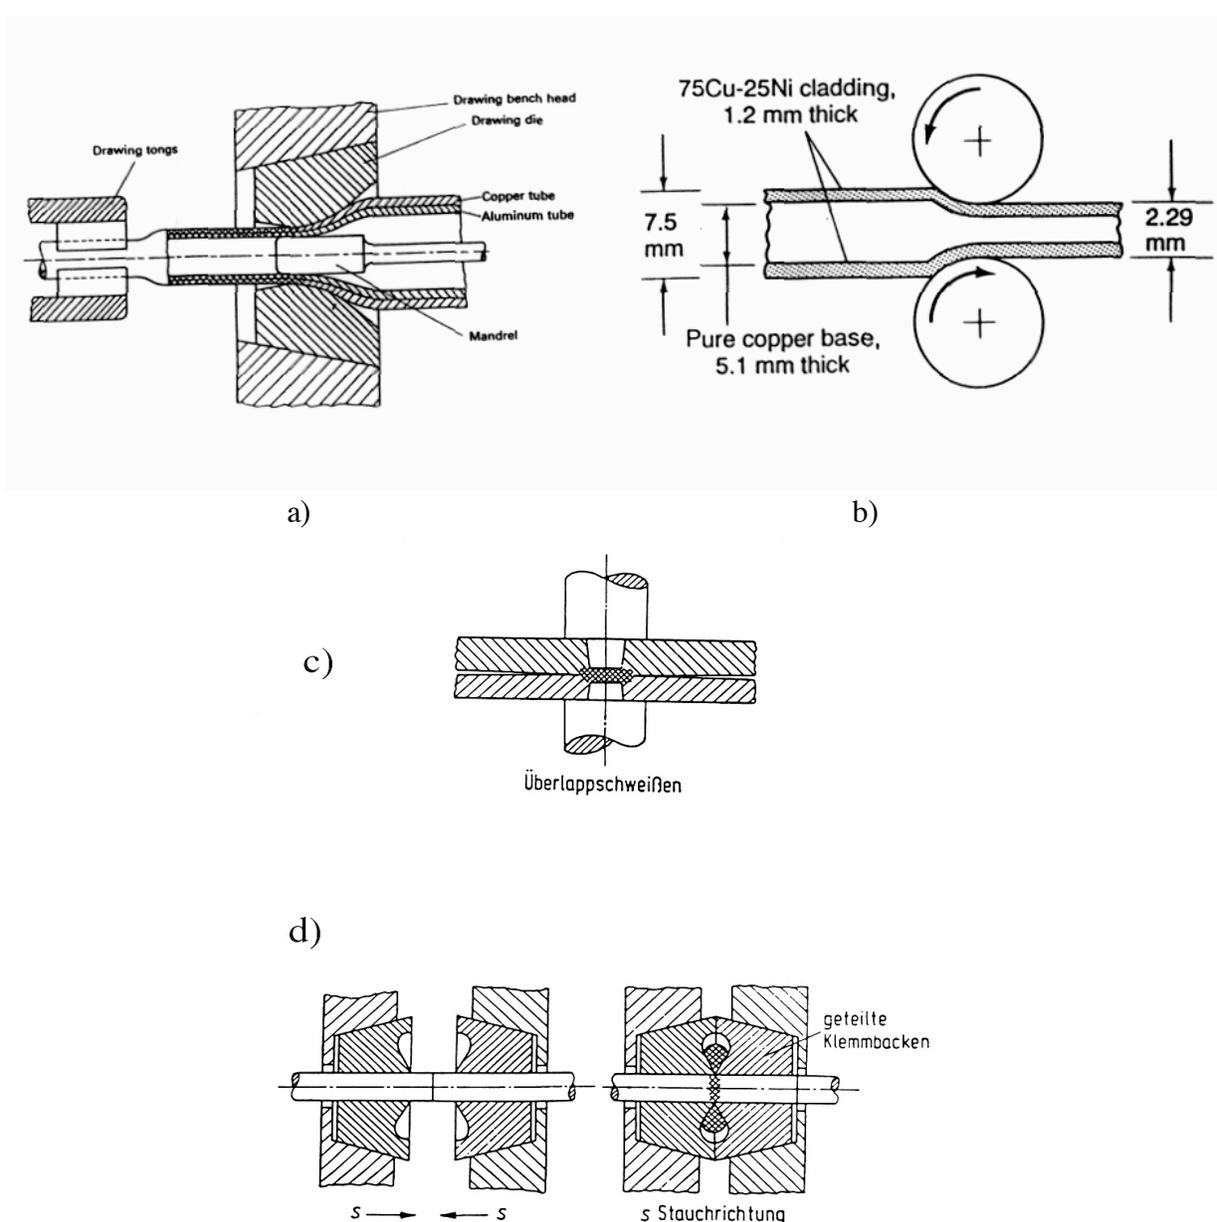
Différentes dispositions du soudage par pression à froid ou à chaud: a) soudage par étirage de deux tubes; b) soudage par laminage, placage; c) soudage par point ou par ligne; d) soudage par forgeage bout à bout.
